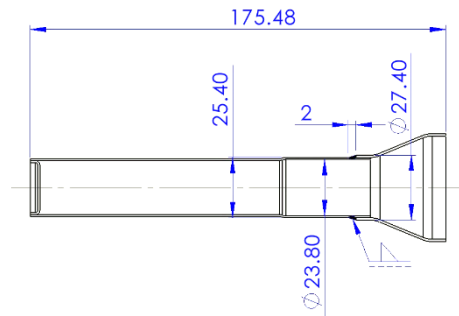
Desain Akhir Assembly Jig Welding
